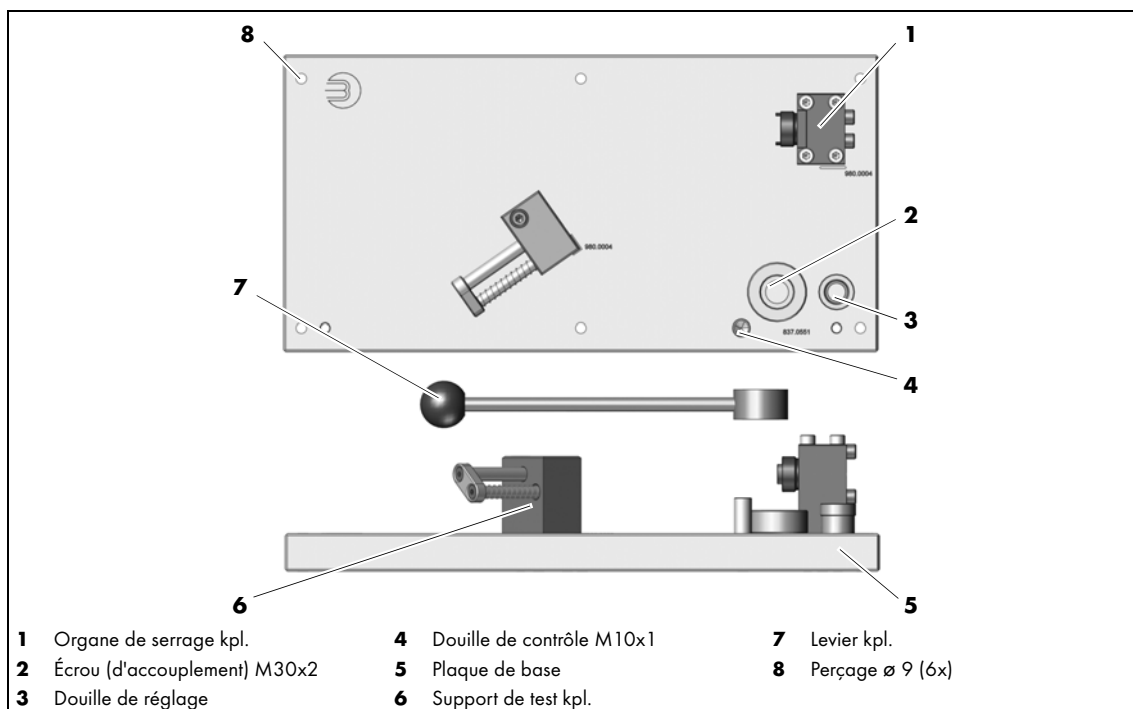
Installer le marbre de contrôle et de rectification ABIROB®350 GC
